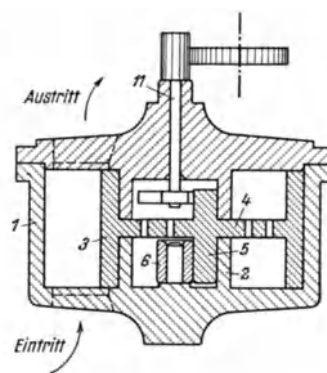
Meßkammer des Ringkolbenzählers, Aufriß.
